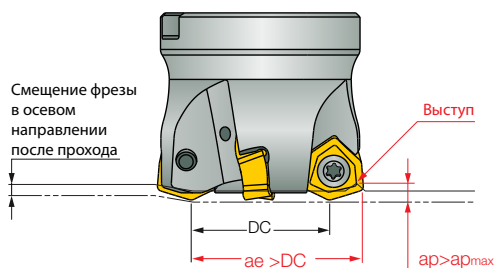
Ширина резания и выступы при фрезеровании с быстрой подачей
